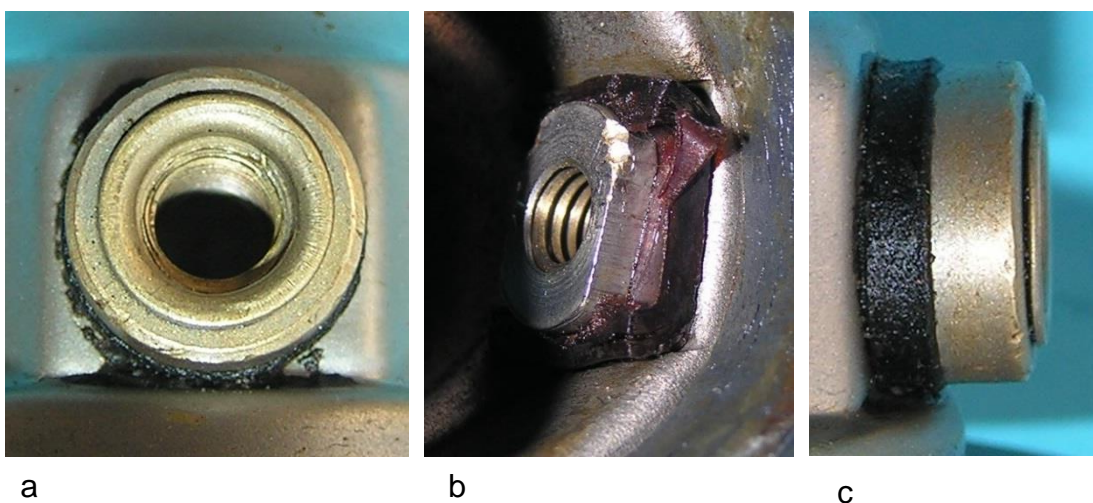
Hülse mit Innengewinde für die Kombination Bürstenhalter und Kabelanschlussbolzen
